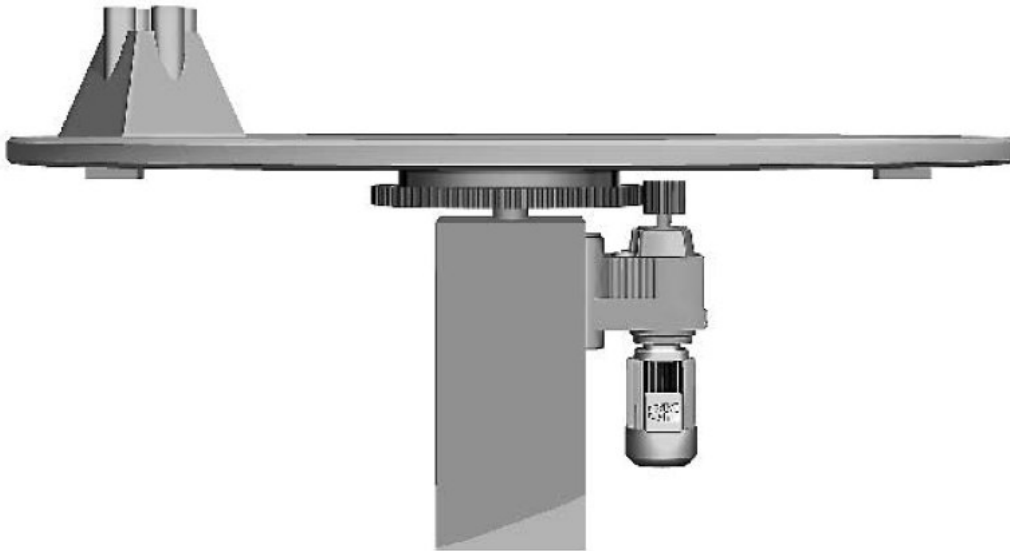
Привод поворотного стола металорізального верстата
